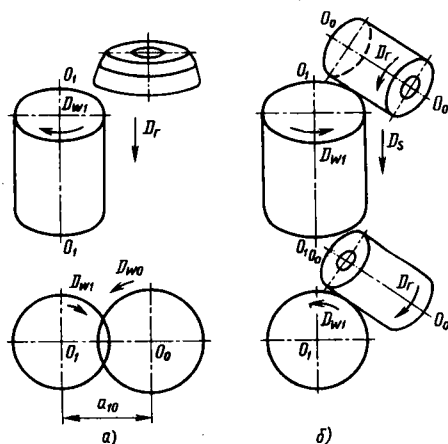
Движения заготовки и обкатного инструмента при параллельных (а) и пересекающихся (б) осях
